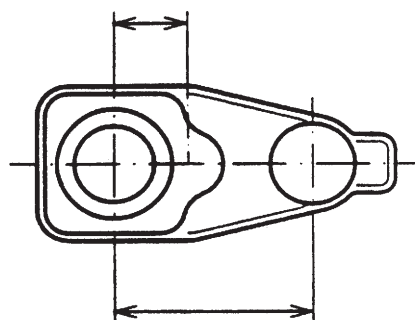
Maße, für welche die Toleranzen für Mittenabstände Anwendung finden
